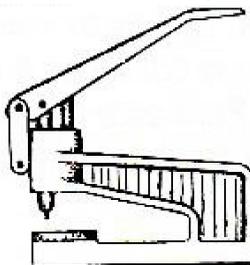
Perfurador utilizado para a furação de placas cobreadas virgens.
